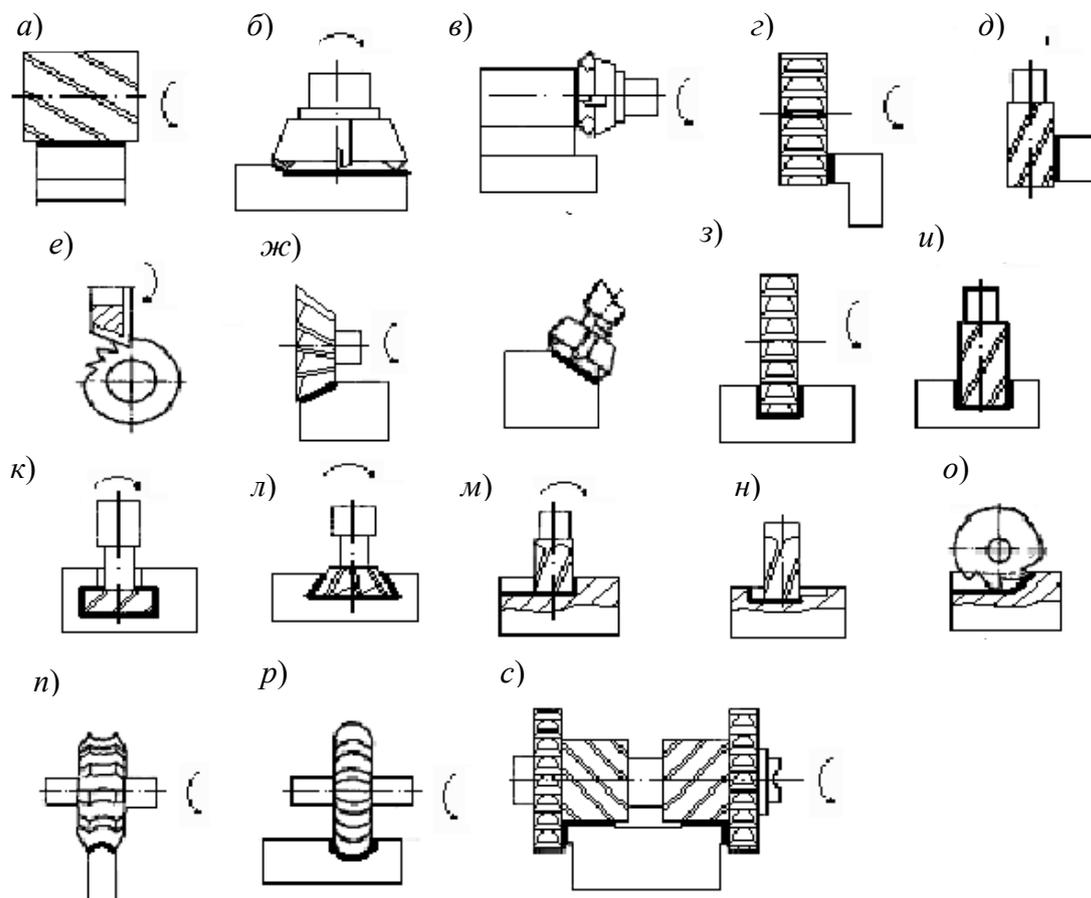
Примеры работ, выполняемых на фрезерных станках
